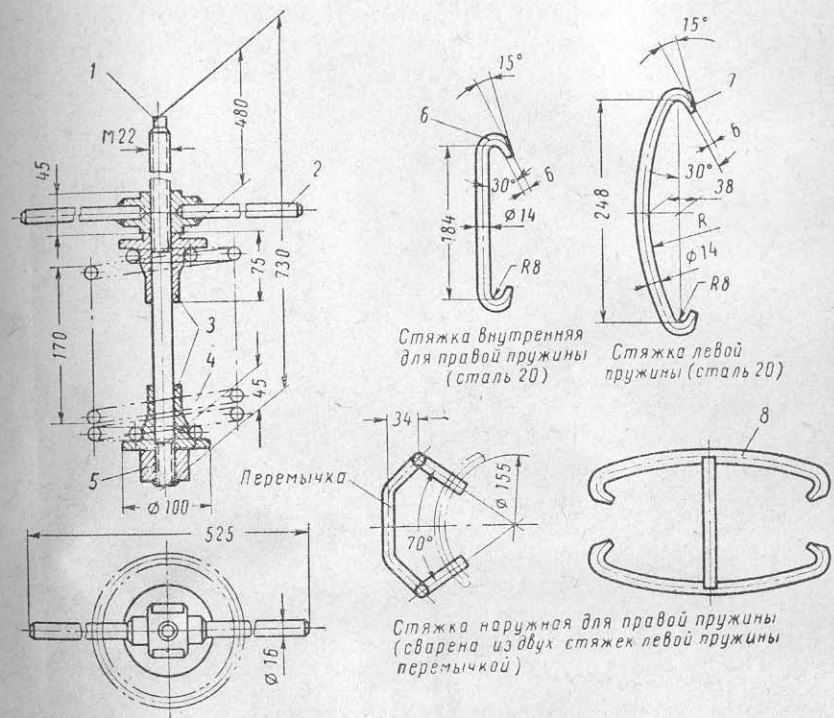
Приспособление для снятия и установки пружин откидывания кабины:
